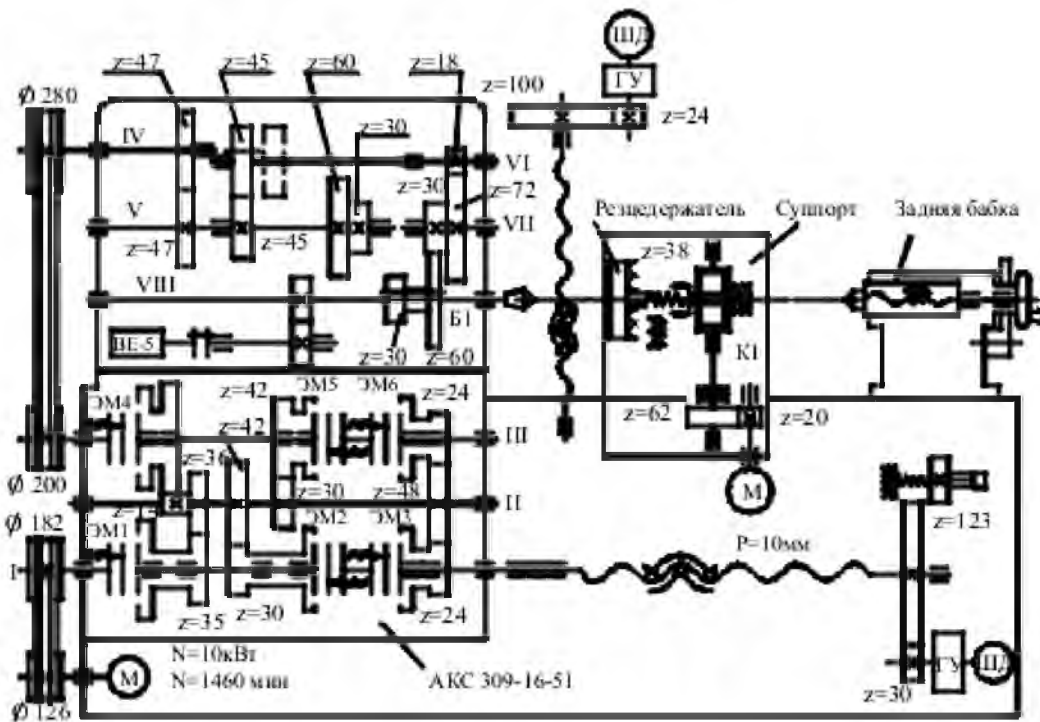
Кинематическая схема станка с ЧПУ
